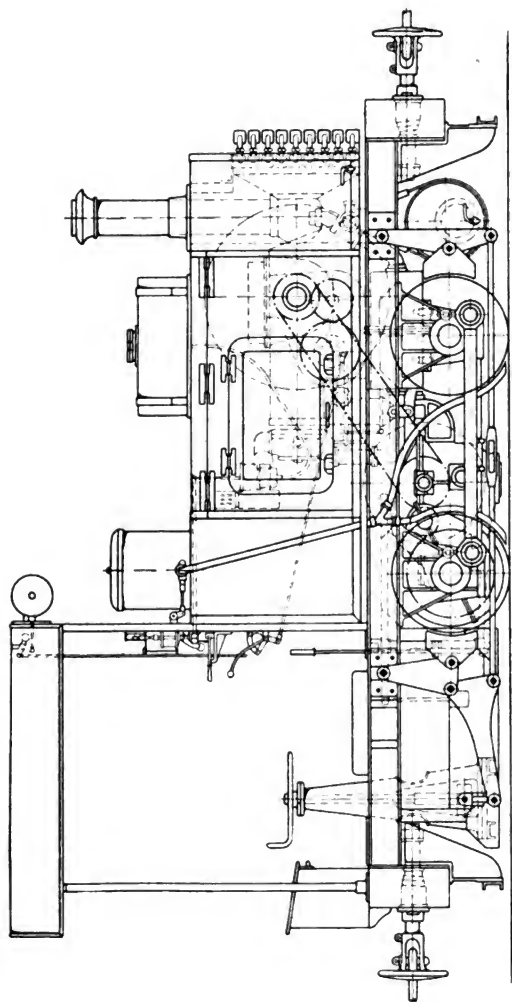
Motorlokomotive der Wolseley Tool and Motor Car Works in Birmingham.
